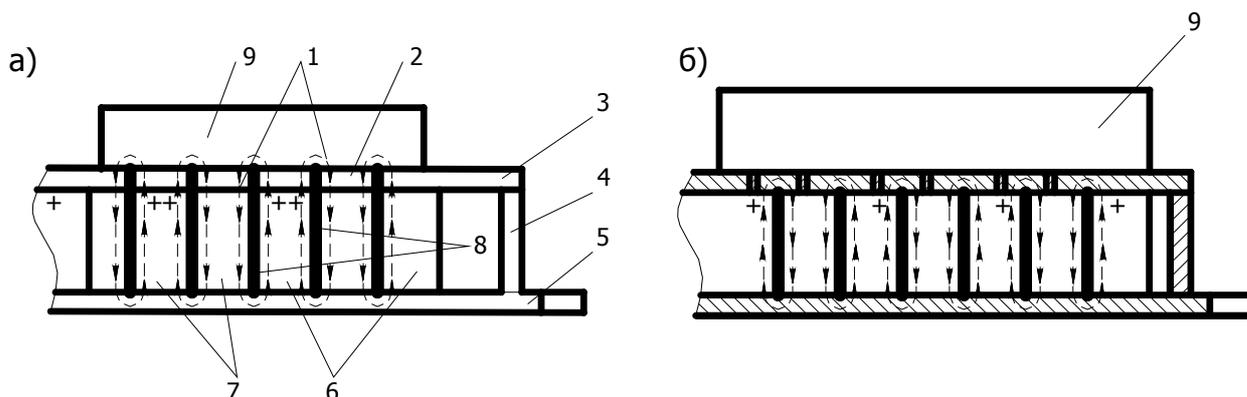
Положение блоков плит с постоянными магнитами: а – при закреплении детали; б – при освобождении детали. 1 – прослойки из немагнитного материала; 2 – полюсные вставки; 3 – верхняя стальная плита; 4 – корпус; 5 – нижняя стальная плита; 6 – постоянные магниты; 7 – пластины из железа Армко; 8 – прокладки из немагнитного материала; 9 – закрепляемая деталь.
